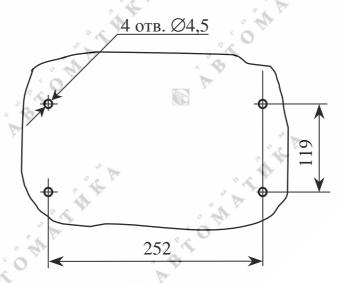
Разметка отверстий для крепления блока преобразовательного
